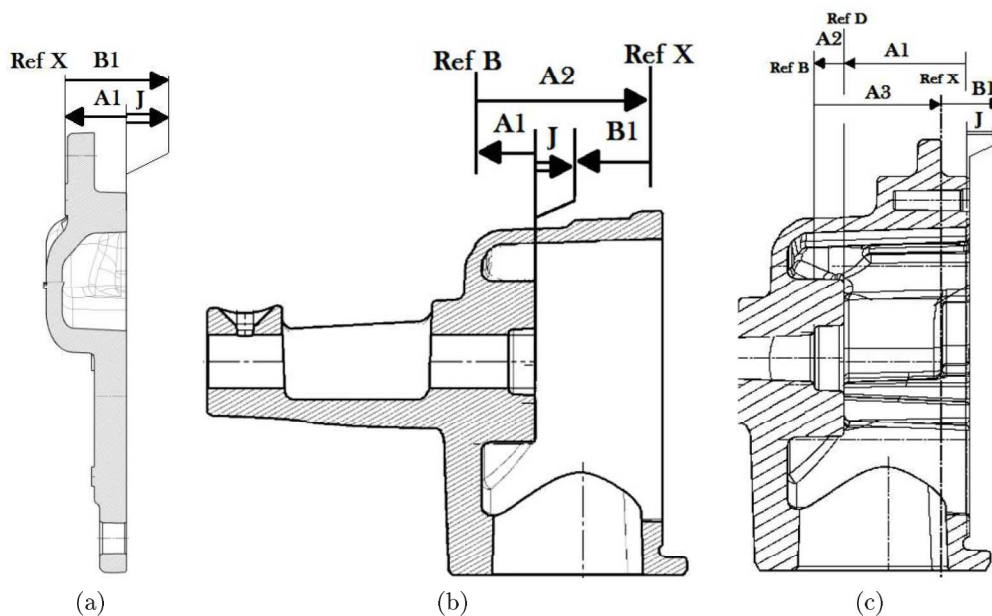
a) Sobre espessura de maquinagem da face de encosto tampa-corpo; b) Sobre espessura de maquinagem do fundo do set hidráulico; c) Sobre espessura de maquinagem da face de encosto corpo-tampa;
